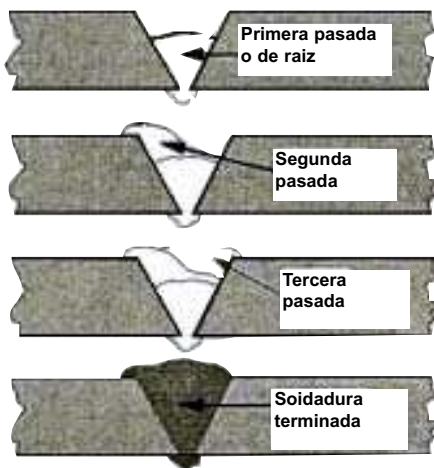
Vista en corte de una soldadura de tres pasadas
